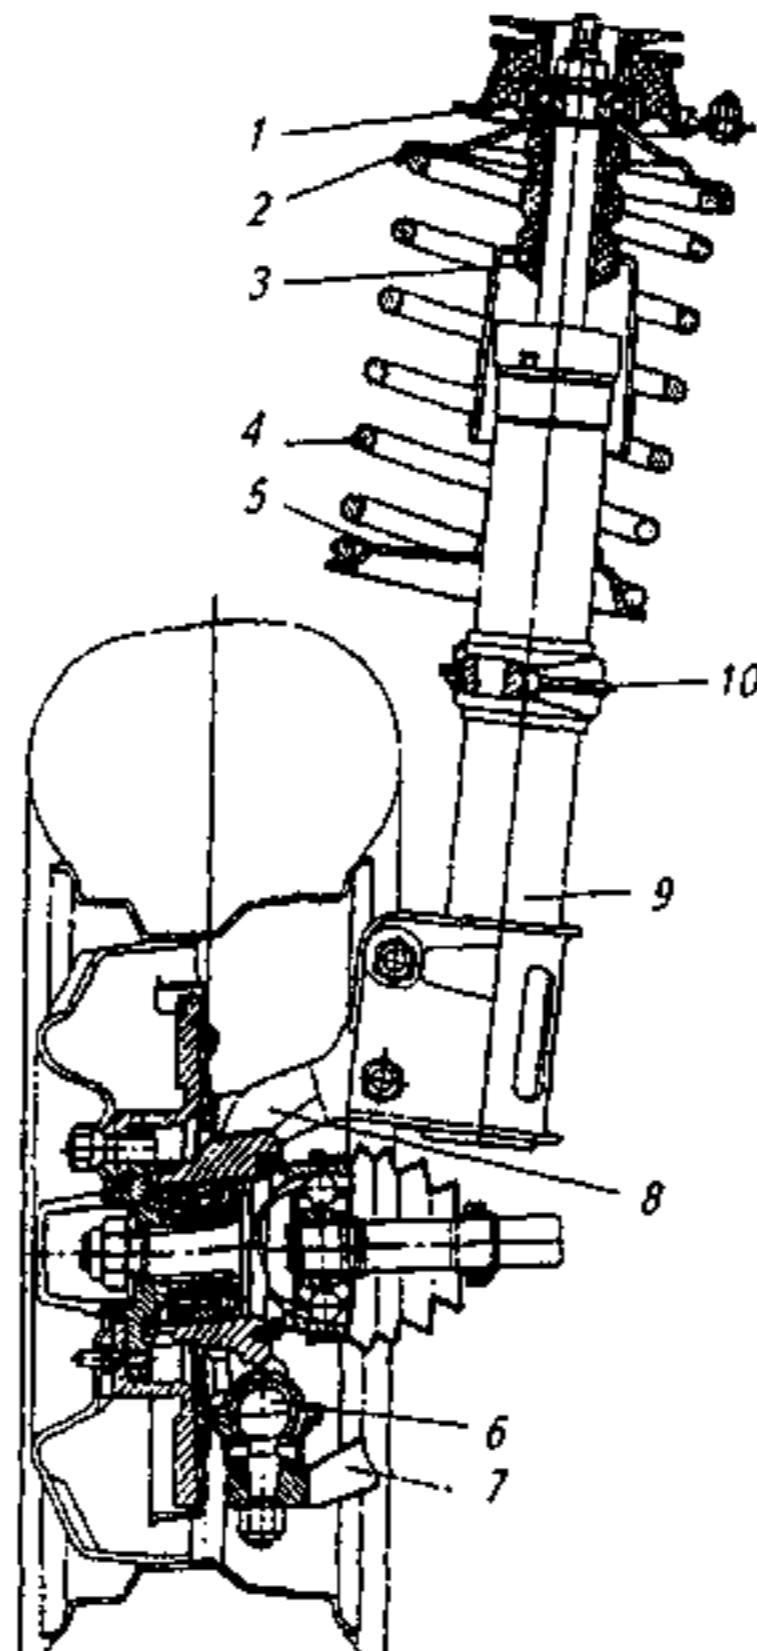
Подвеска автомобиля ВАЗ-2108: 1 – подшипник верхней опоры; 2 – чашка верхней опоры; 3 – буфер сжатия; 4 – пружина; 5 – чашка нижней опоры; 6 – шаровая опора; 7 – нижний рычаг; 8 – ступица; 9 – амортизированная стойка; 10 – поворотный рычаг
